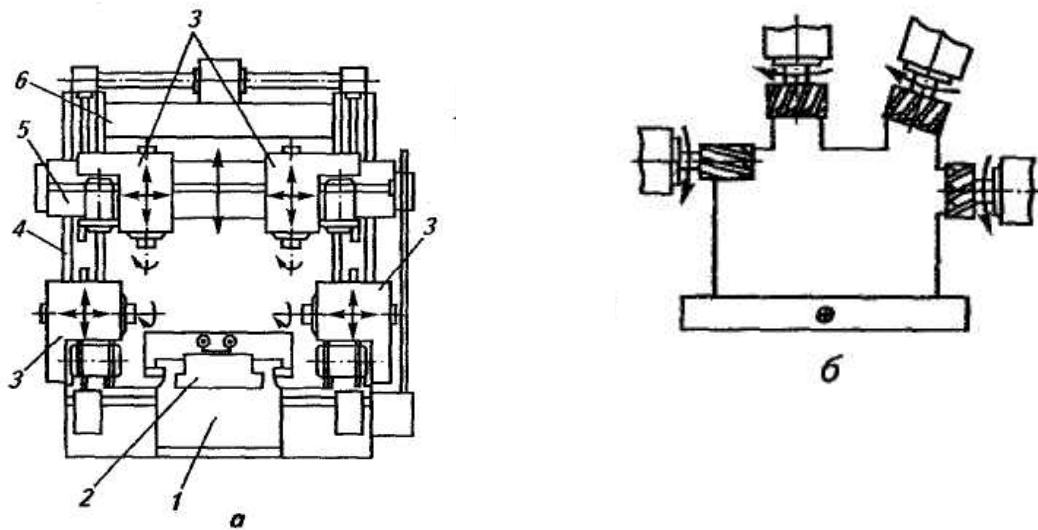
Общий вид продольно-фрезерного двухстоечного станка (а) и схема обработки заготовки (б): 1 - станина; 2-стол; 3-фрезерные головки; 4 - стойка; 5- траверса; 6- поперечина
